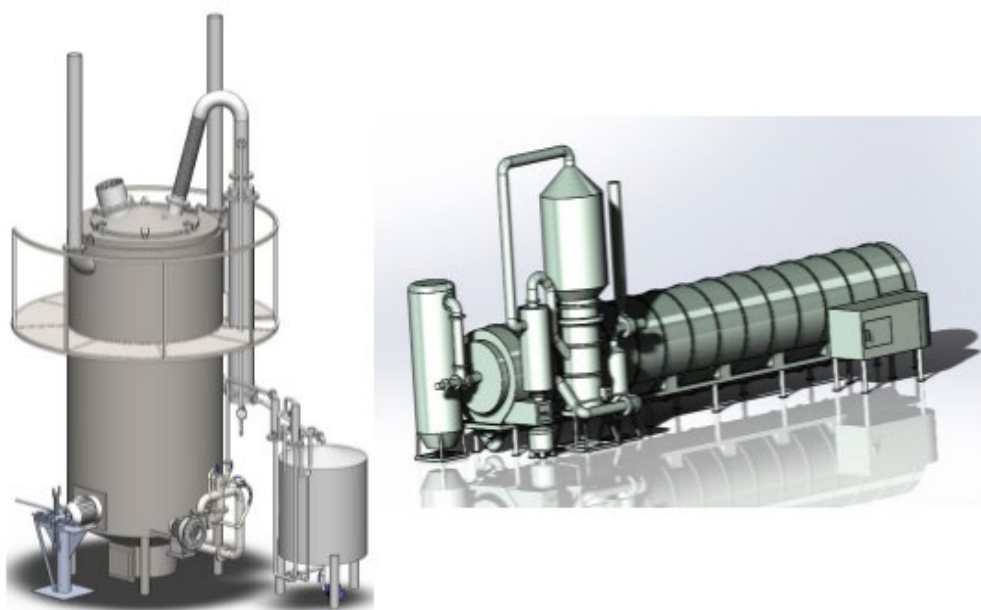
Установа для переробки нафтошламу Фортан-М
